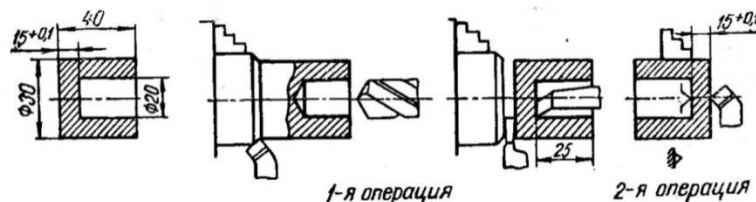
Обработка стакана из прутка при высокой точности толщины дна.
